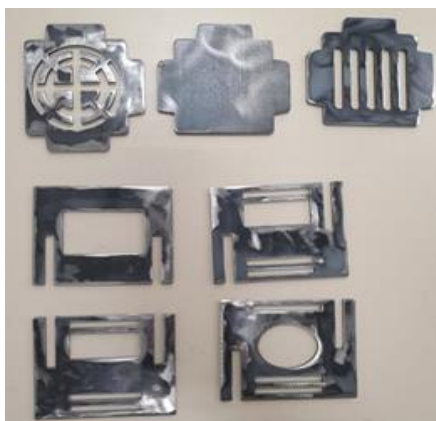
Детали сборочной единицы подставки «Таганок»
